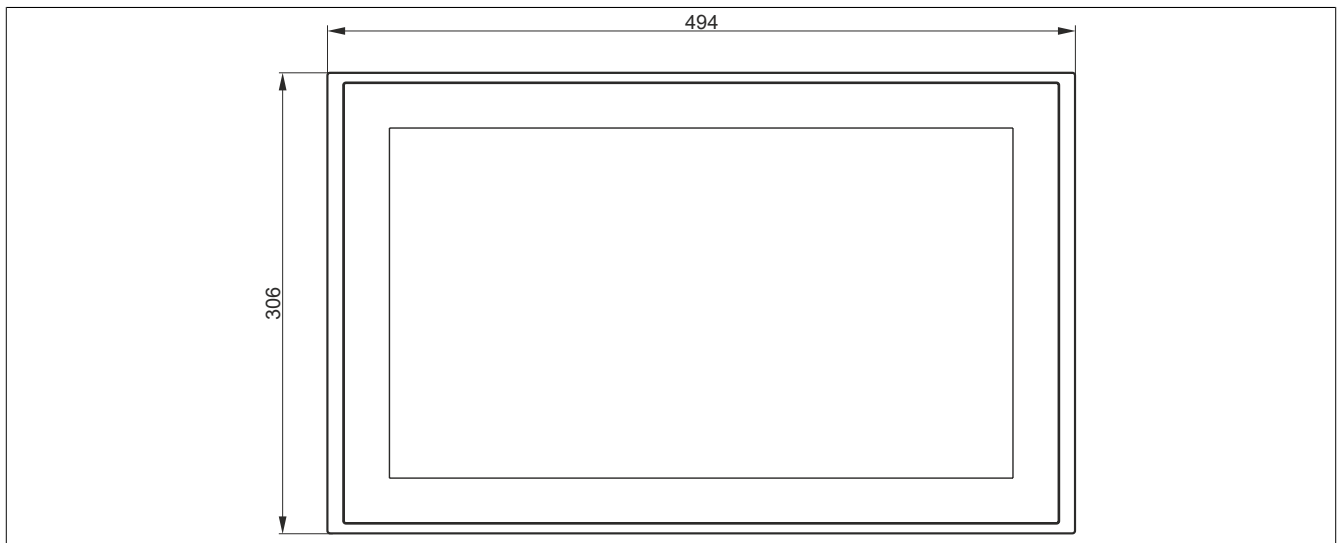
5AP5130.185B-000 - Abmessungen
